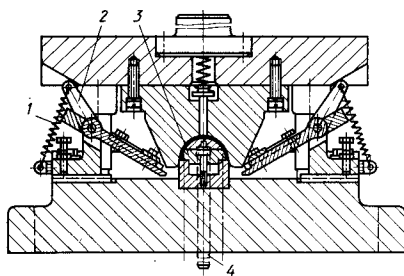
Схема гибки П-образной детали с верхним расположением матрицы
